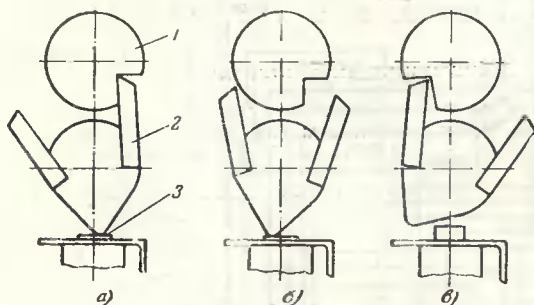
Положение блокировочного кулачка разъединителя.
